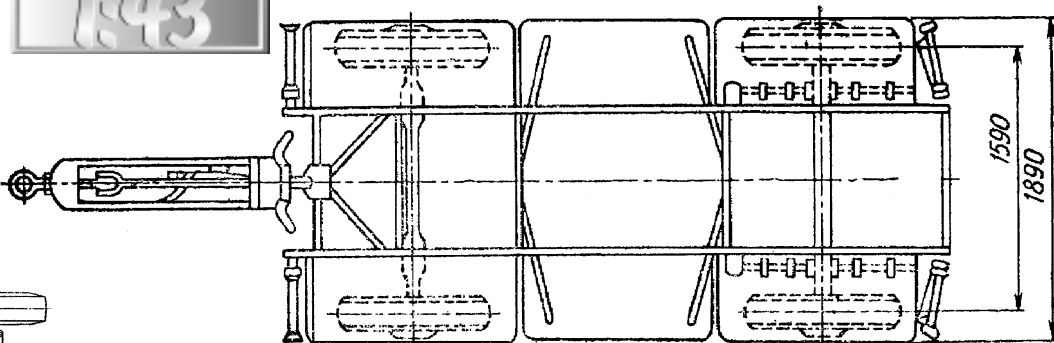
Привод тормозов и привод поворота передних колес прицепов СМЗ-710В и СМЗ-710Б
